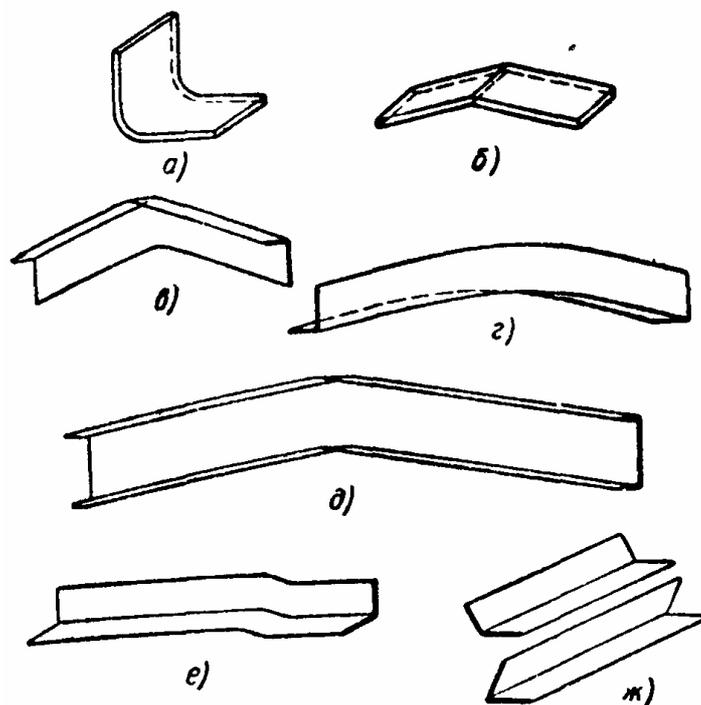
Виды горячей гибки деталей плоских конструкций:
